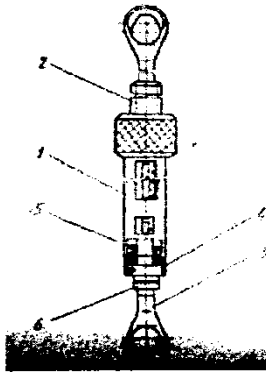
Пристрій КИ-6296 для перевірки натягнення гусеничного ланцюга:
